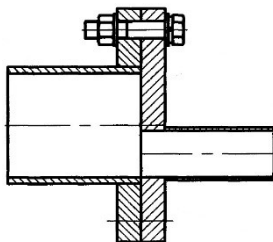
Фланцеве з'єднання згідно з пат. № CN202538408U
